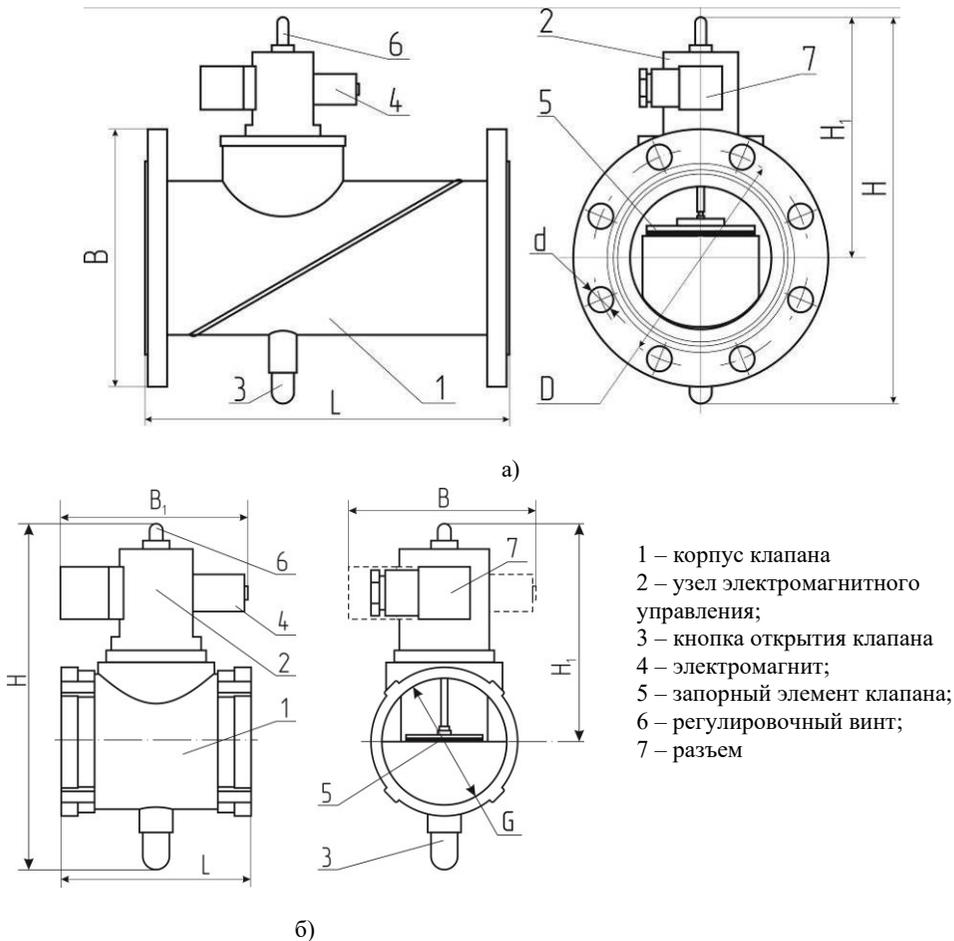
Внешний вид клапана: а) фланцевый; б) муфтовый
